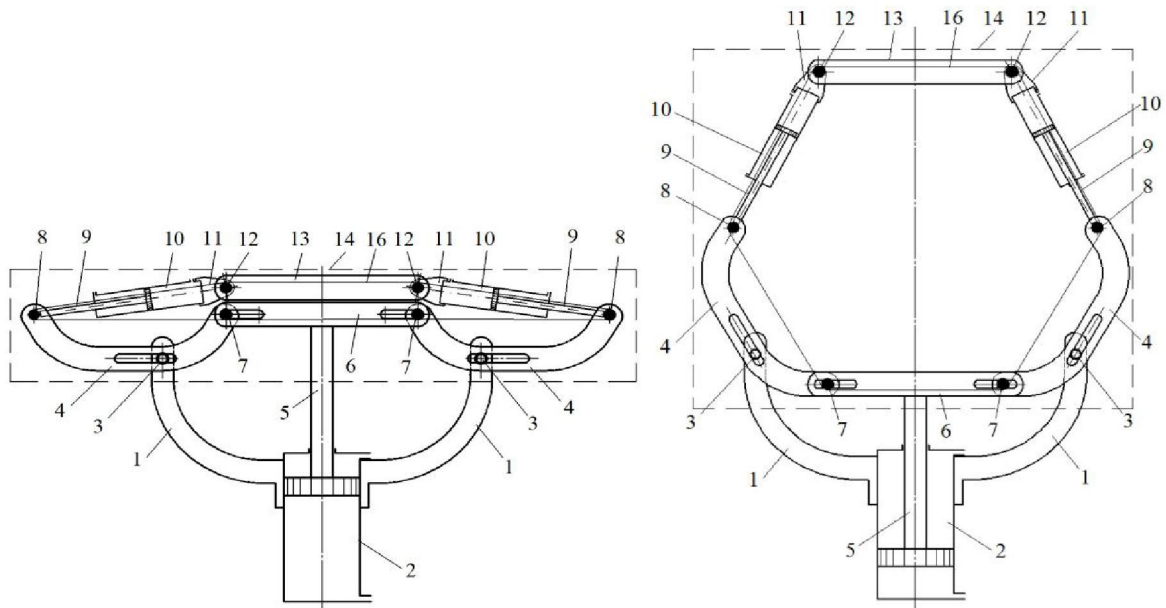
Рычажно-шарнирное захватное устройство в двух положениях:
